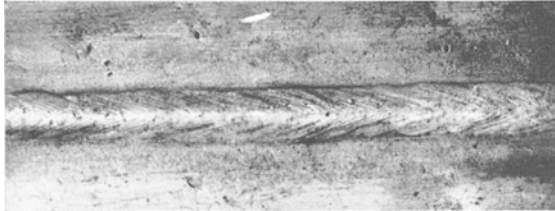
Aluminium-Schweißnaht (5 mm-Blech).
